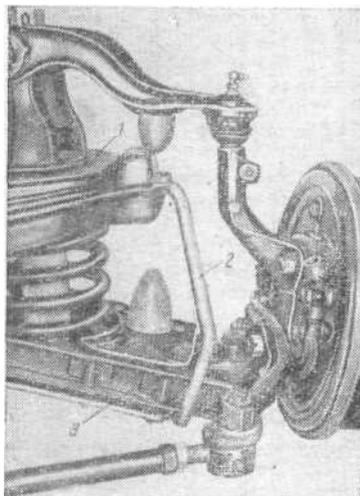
Установка предохранительной; стяжки для блокировки пружины передней подвески
